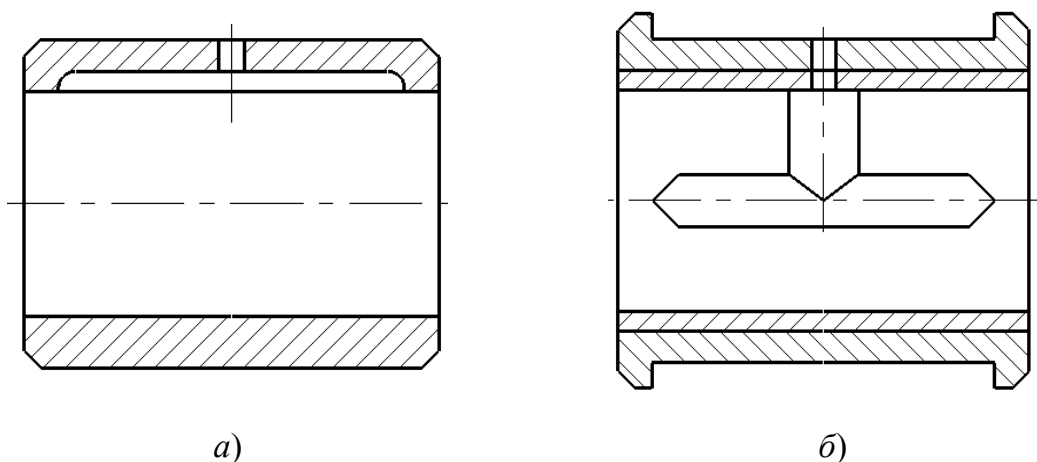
Конструкция вкладыша подшипника скольжения:
